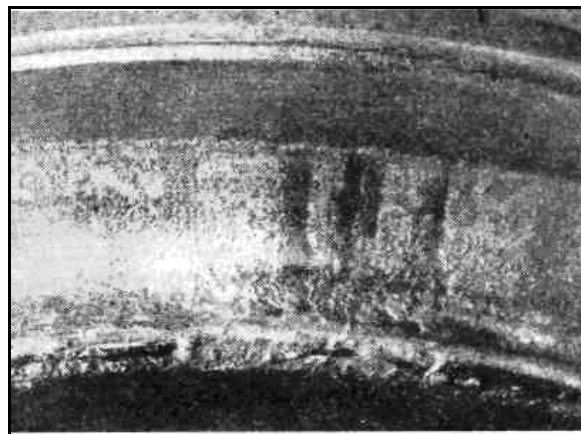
Следы фреттинга на рабочей поверхности кольца подшипника.
